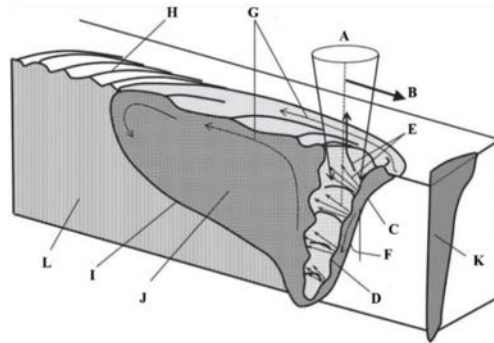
Schéma représentant un keyhole en vue de coupe, d'après [96]. A : Faisceau laser ; B : Direction du soudage ; C : Front avant le keyhole ; D : Bosses du front avant ; E : Jet de vapeur ; F : Inclinaison du front avant ; G : Déplacements convectifs du bain ; H : Structure en chevrons ; I : Front de solidification ; J : Bain de fusion ; K : Projection d'une moitié du profil du keyhole ; L : Matériau resolidifié.
